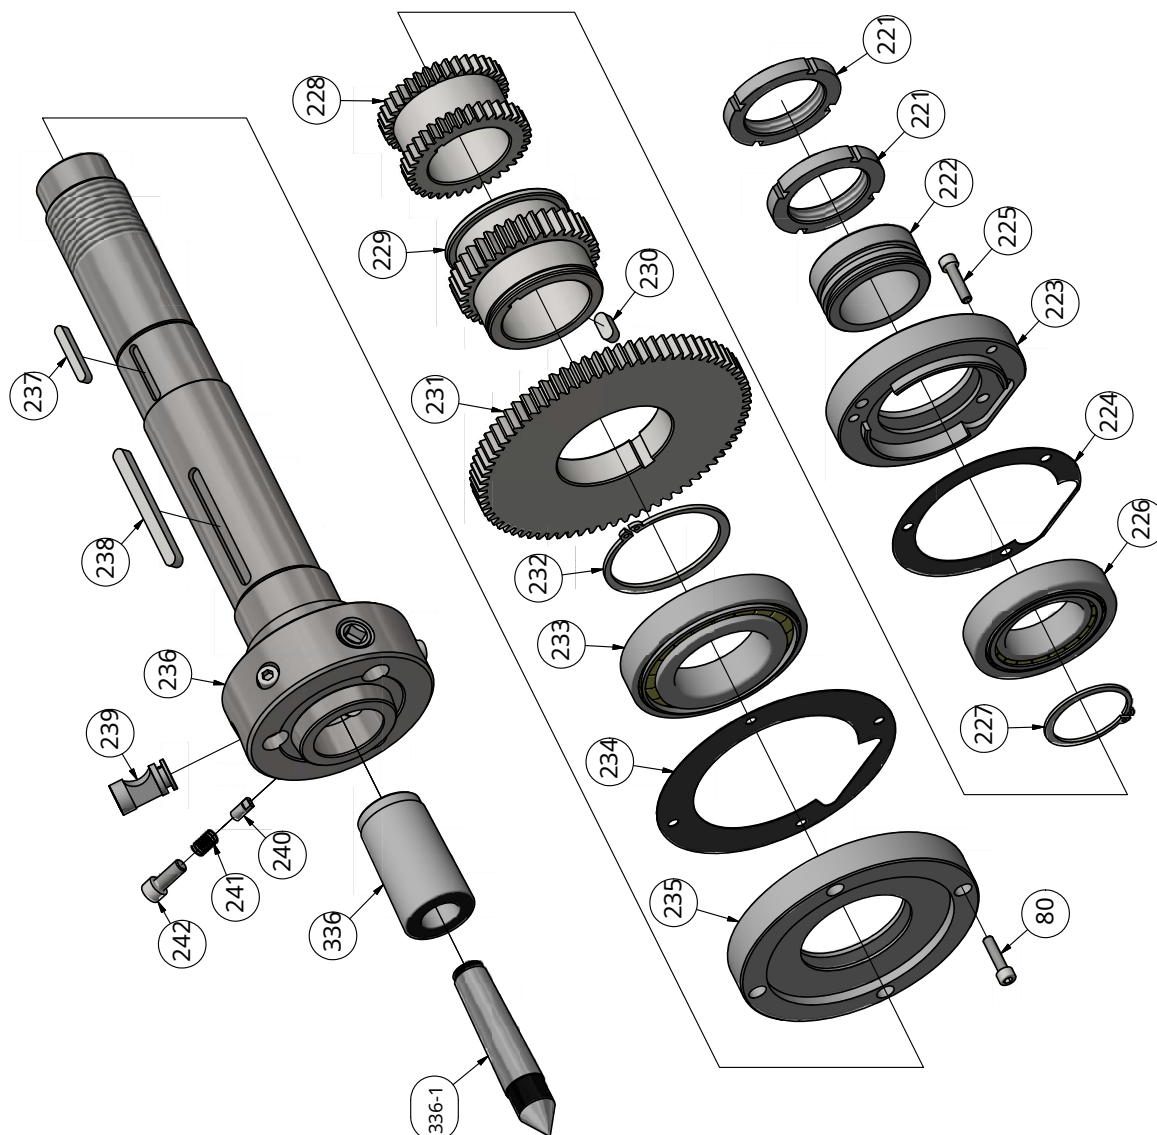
Getriebe Spindelstock 3-6 - Engranaje del cabezal 3-6
